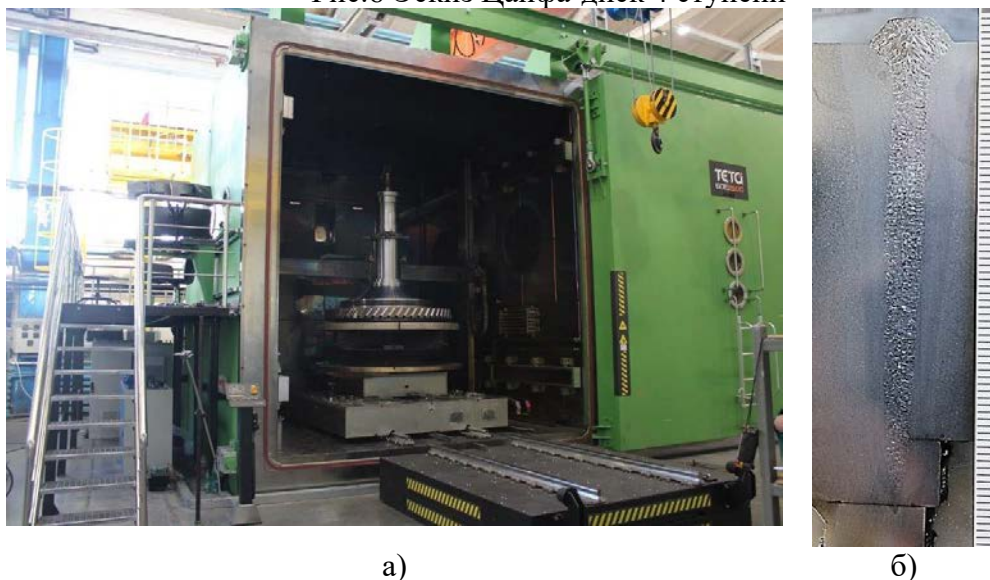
Фотография установки с деталью и вид сварного шва:
